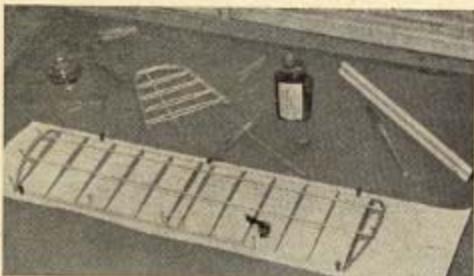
Stavba křídla — provedení střední části, lepení stojin a pouzder.
